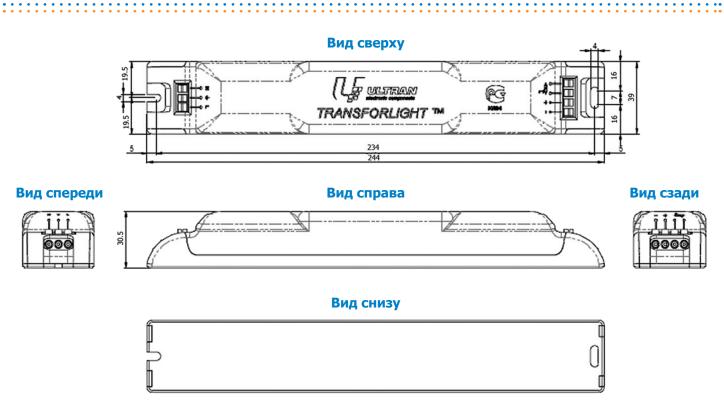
Габаритные, установочные и присоединительные размеры ИП
